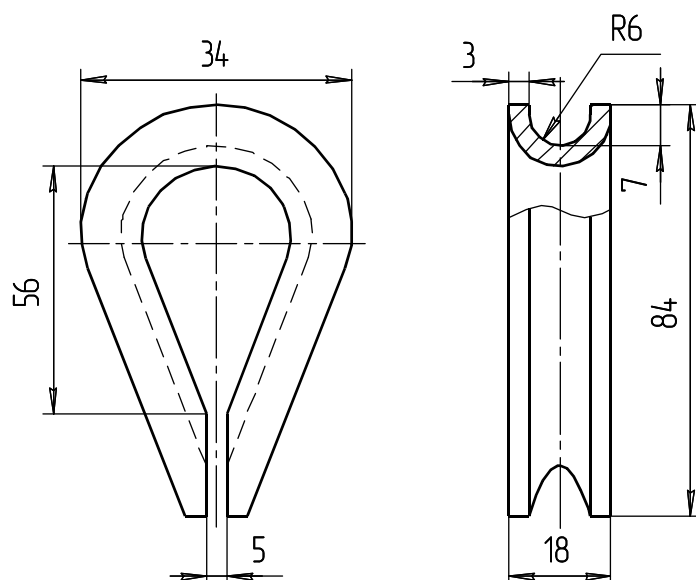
Эскиз коуша по ГОСТ 2224—93
